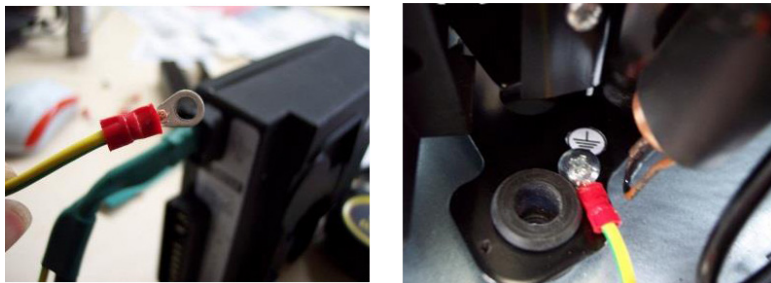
Particolare connessione cavo di terra sulla parte metallica del compressore
